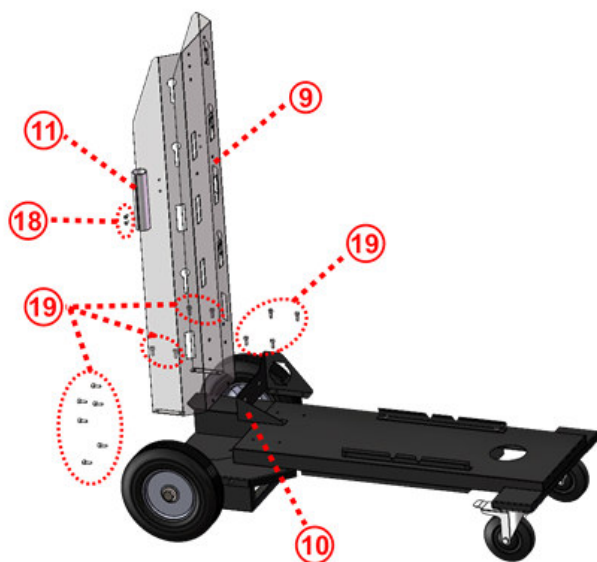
Montage des Schweißgerätwagens Schritt 2, 3 & 4
